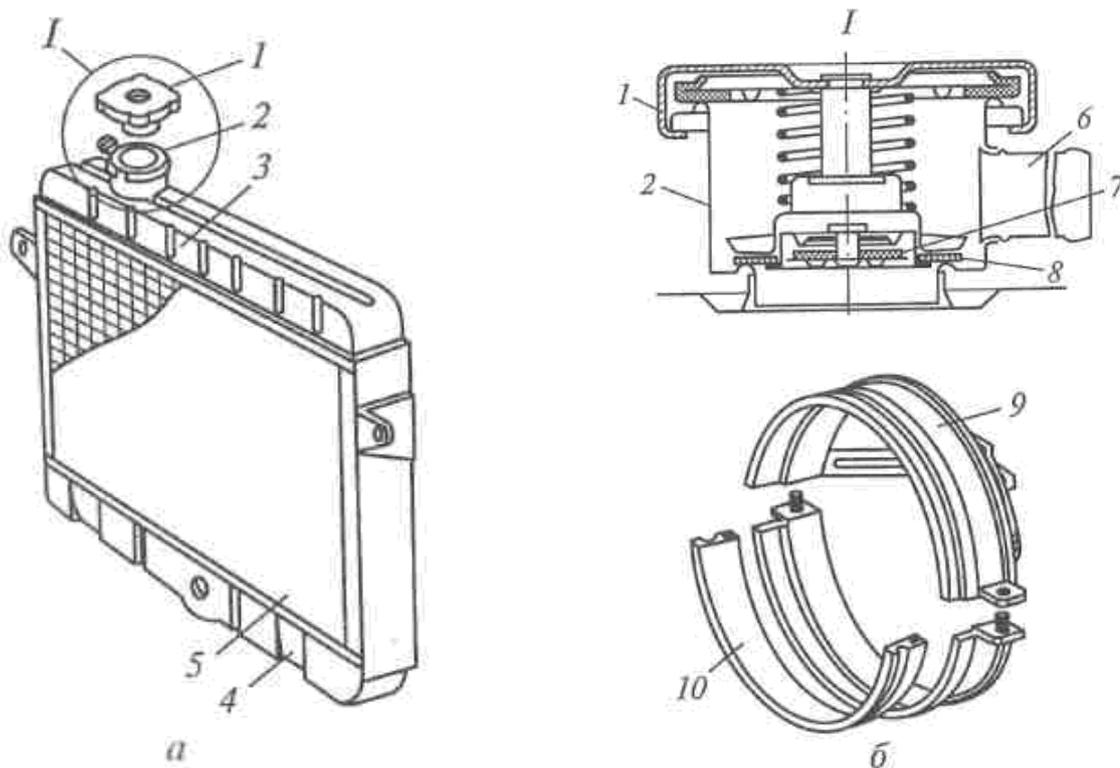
Неразборный радиатор (а) кожух (б) вентилятора двигателя: 1 - пробка; 3 – горловина; 3,4 – бачки; 5 – сердцевина; 6 – патрубок; 7,8 – клапаны; 9 – кожух; 10 – уплотнители.
